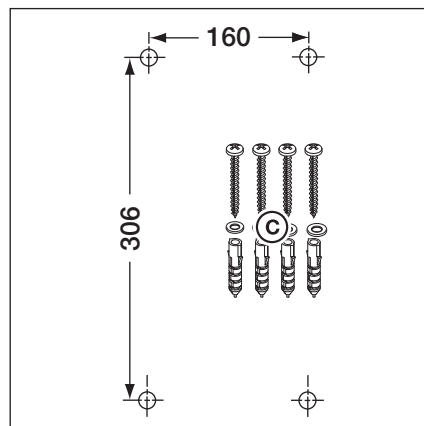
Схема расположения отверстий для крепления, необходимый монтажный материал
